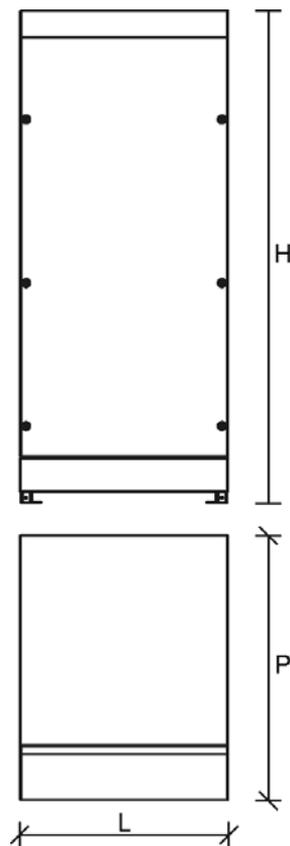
Dimensioni armadio batteria esterno Tipo 1
